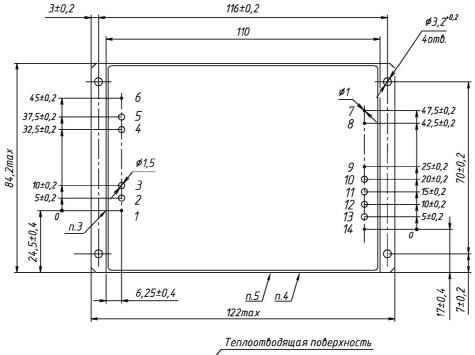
Модуль типа MDV-160 одноканальный, корпус с фланцами Общий вид
